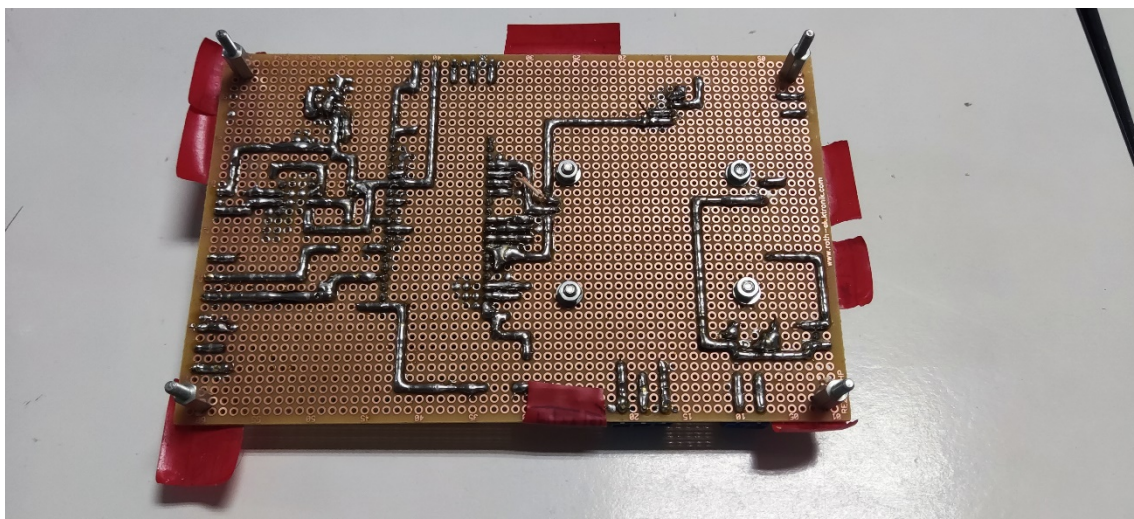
Reverso de sistema de medición soldado en placa perforada
